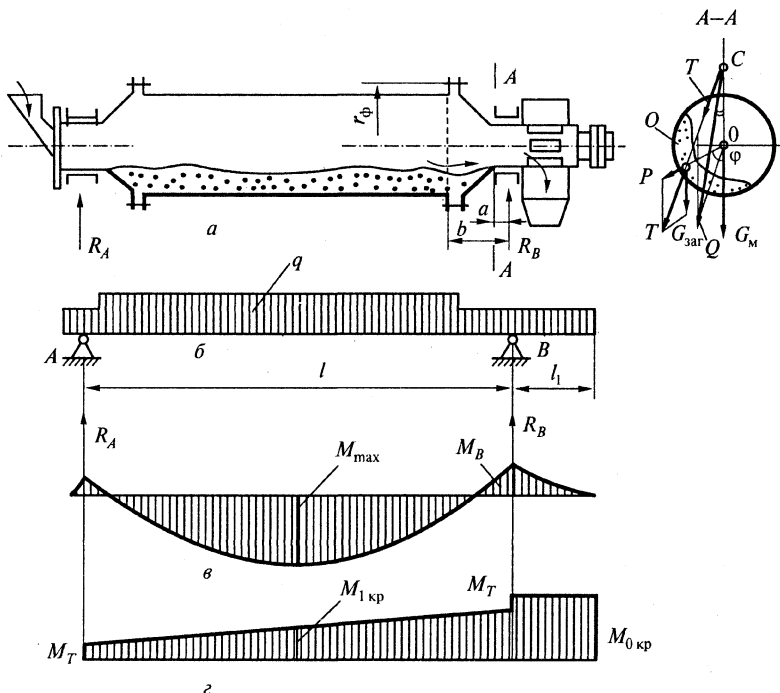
Схема к расчету нагрузок барабанной мельницы:
